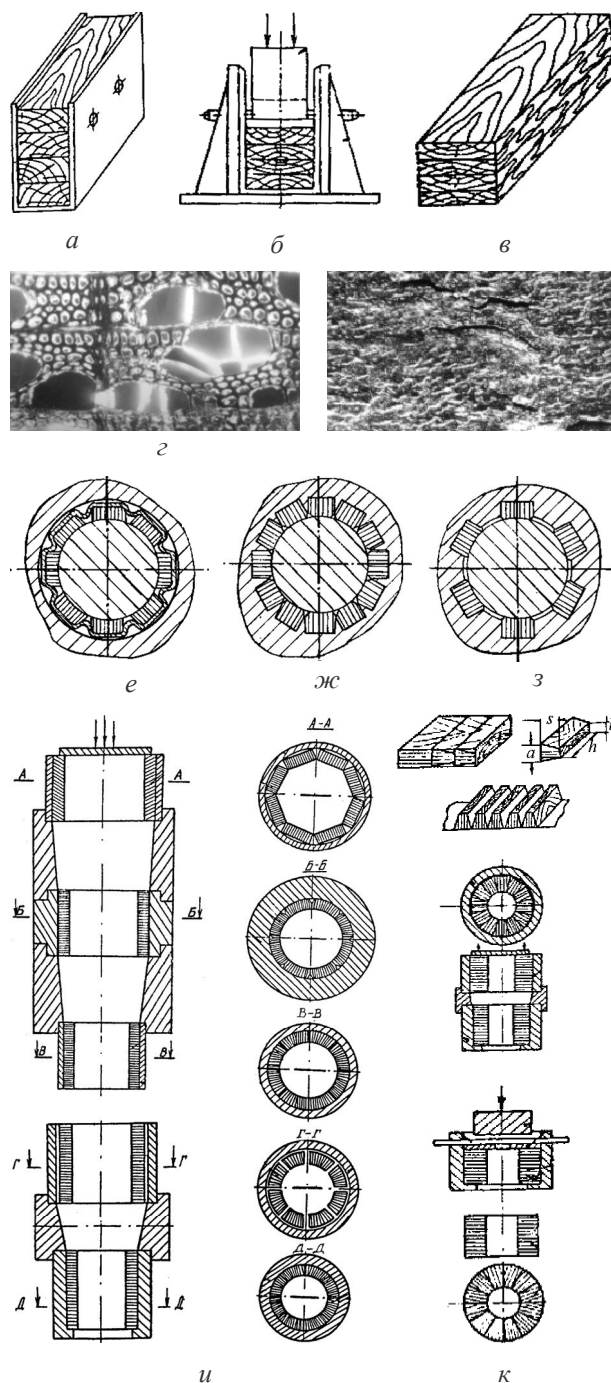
Кассета (а), пресс-форма (б), прессованная заготовка (в), микроструктуры торцевого среза древесины до (д) и после (д) прессования (ув. 350×), наборные подшипники с прямоугольными брусками: запрессованными в пазы металлической обоймы (е, ж); собранные в тонкостенном металлическом сепараторе, запрессованном в посадочное место ступицы (з). Устройства для получения ПС вкладышей из брусков ДП-О прямоугольных (и) и трапециевидных (к)
